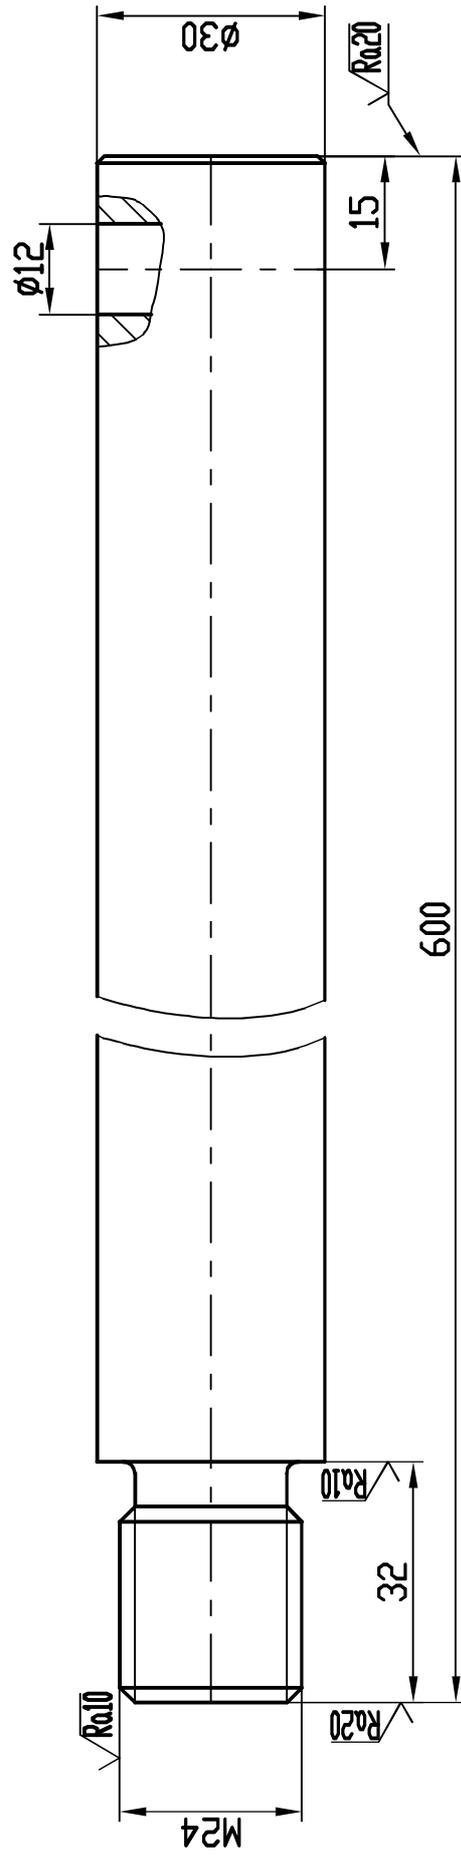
Приспособление для демонтажа коробки скоростей из стойки
